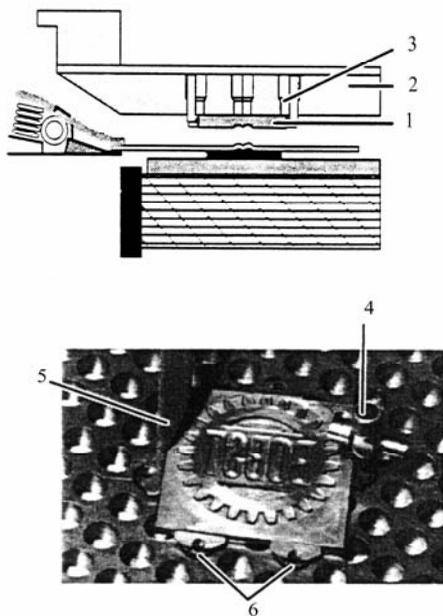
Сотовая рама для крепления штампов: 1 — штамп для тиснения; 2 — рама; 3 — крепежный крючок; 4 — гаечный ключ для затяжки крючка; 5 — рычаг; 6 — крепежные крючки
